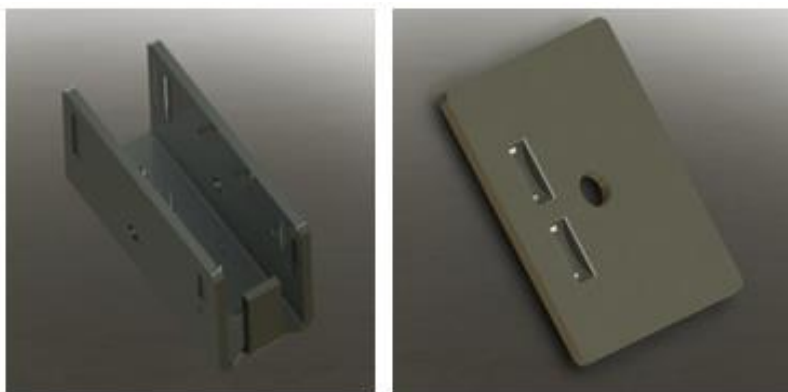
Soporte de carril y yunque de engrapadora de tipo pesado desarrollada para la cátedra tecnología industrial III
